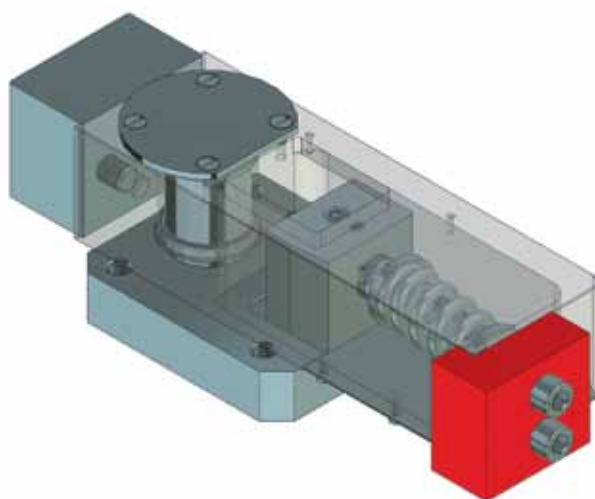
Центробежный выключатель ПРУ с дополнительным проверочным грузом
